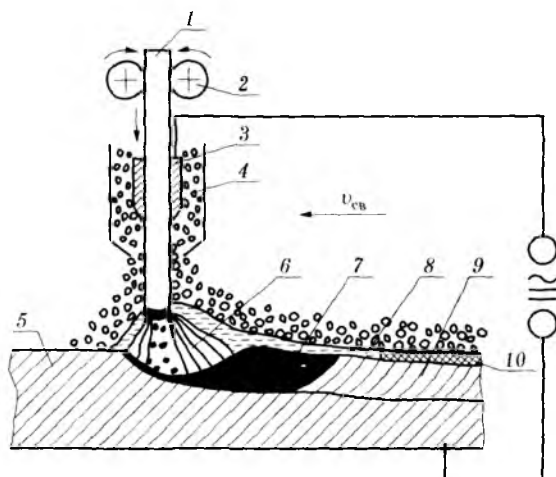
Схема автоматической сварки под флюсом:
